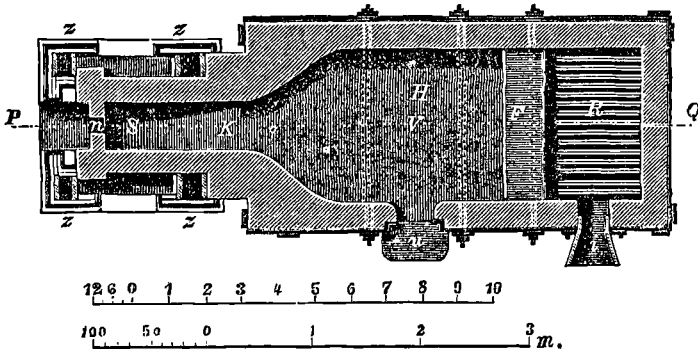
Four à souder avec foyer à grille; coupe horizontale suivant MN (Fig. 339). (Echelles en pieds du Rhin et en mètres.)
